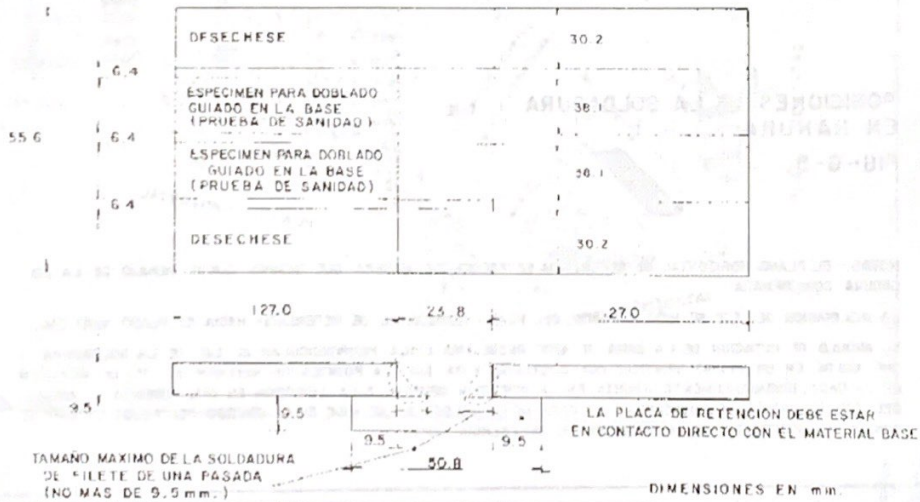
SOLDADURA DE ENSAYO PARA PRUEBAS DE SANIDAD (UNICAMENTE PARA CALIFICACION DE SOLDADORES)
